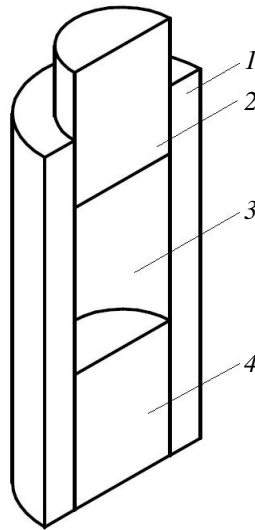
Специальное приспособление для измерения ТКЛР порошковых материалов: 1 – втулка; 2 – верхняя заглушка; 3 – место размещения образца; 4 – нижняя заглушка
